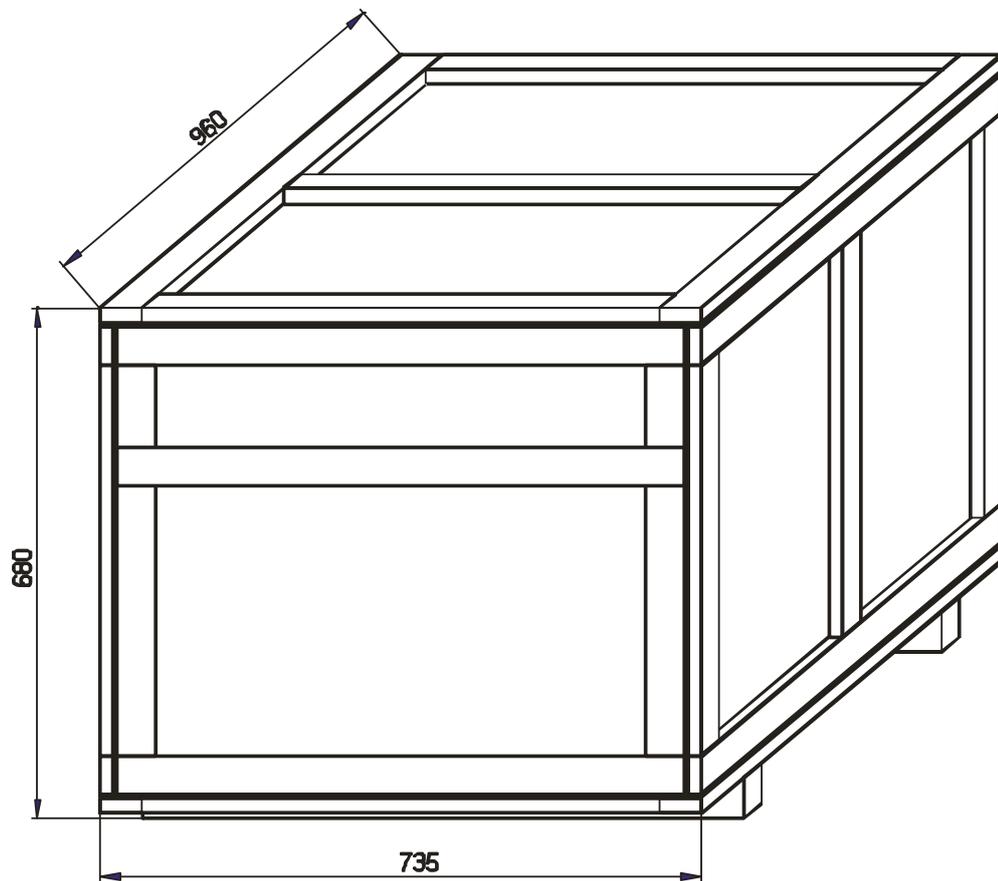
Габаритные размеры ящика транспортного ЯКУР.321213.002
